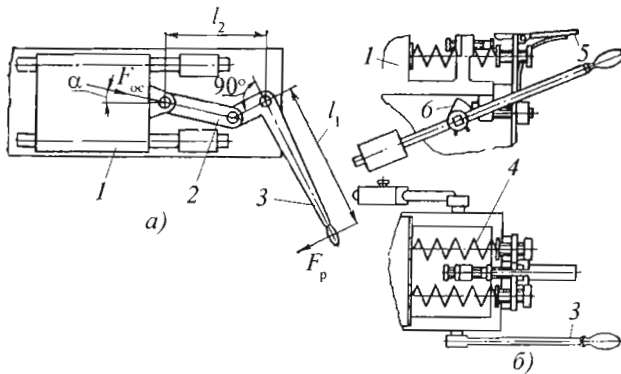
Рычажный (а) и полуавтоматический пружинный (б) приводы маломощных стыковых машин: 1 – подвижная плита; 2 – серьга; 3 – рычаг; 4 – пружина механизма осадки; 5 – защелка; 6 – эксцентрик;  $F_p$  – сила рычага
